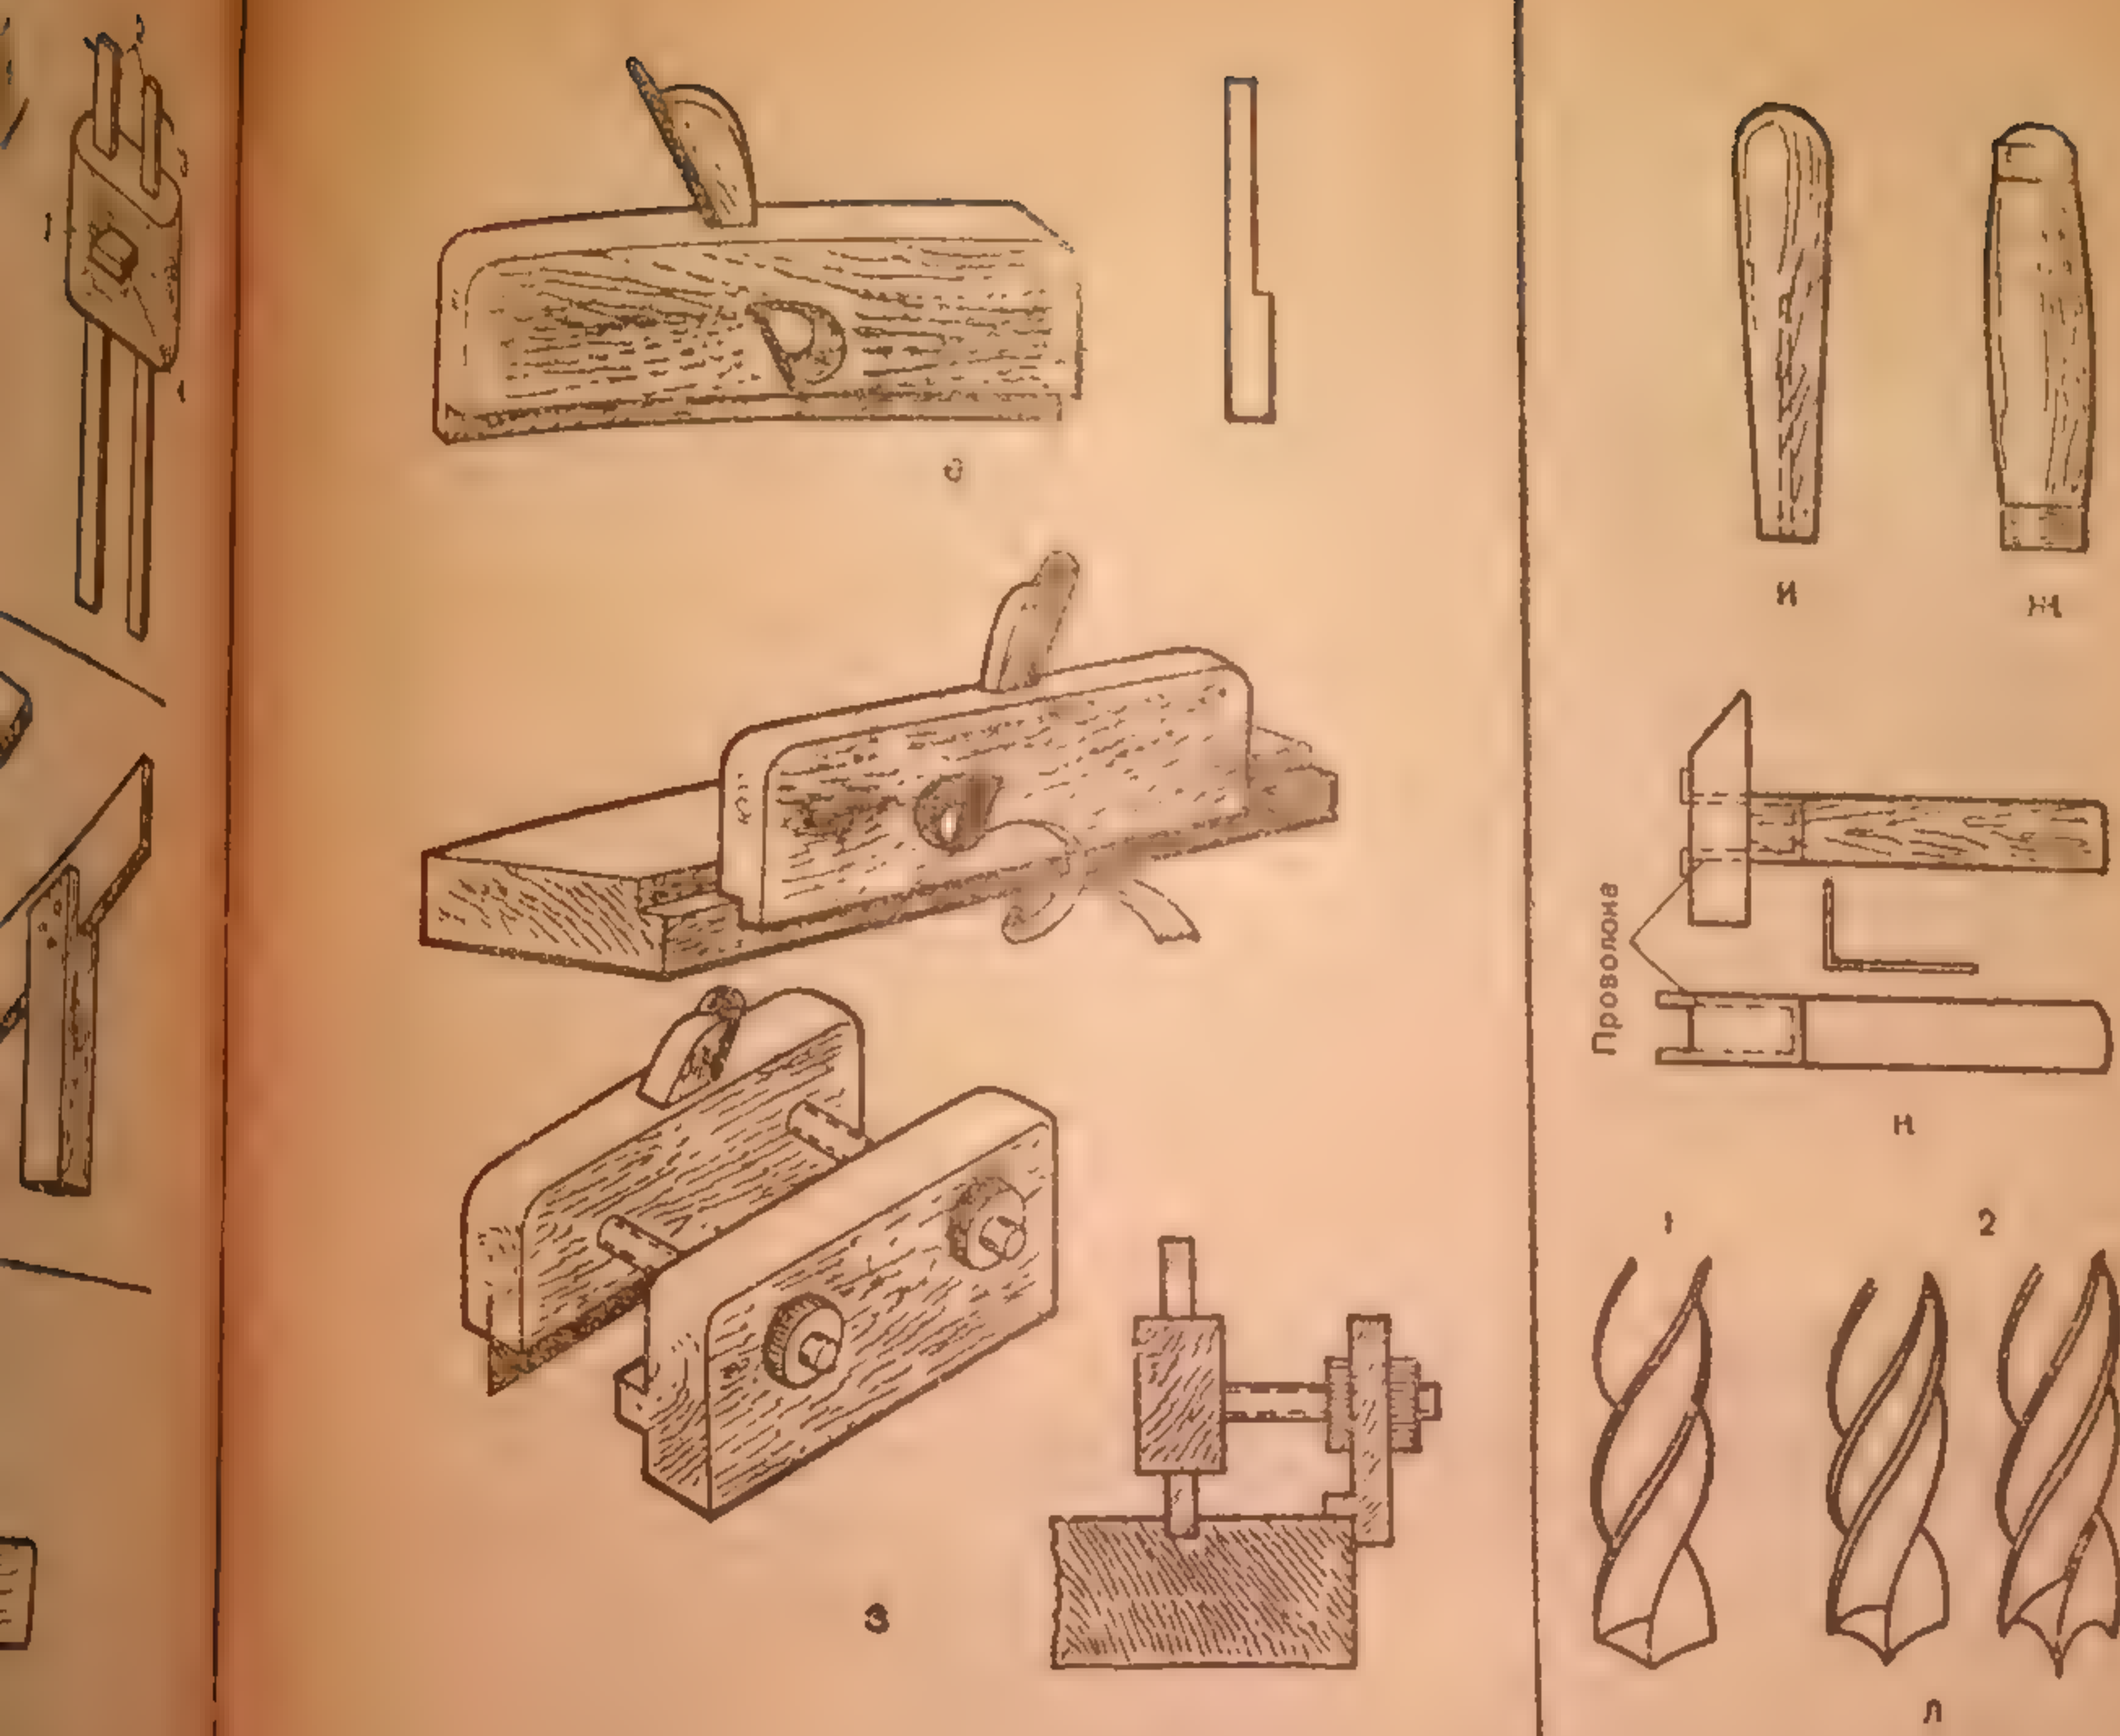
Изготовление некоторых приспособлений и инструментов для обработки дерева:
